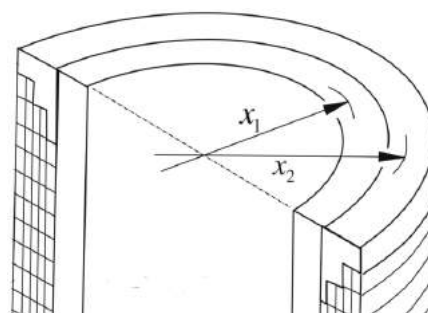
Царга, образованная из узкой заготовки прямоугольного поперечного сечения
